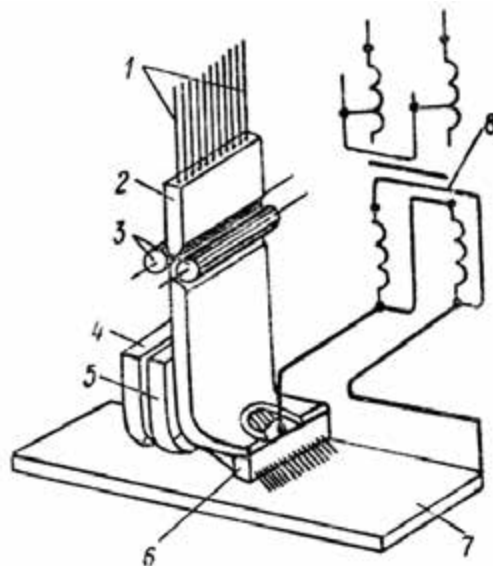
Схема наплавлювальної головки АМН-3 для багатоелектродного наплавлювання:
